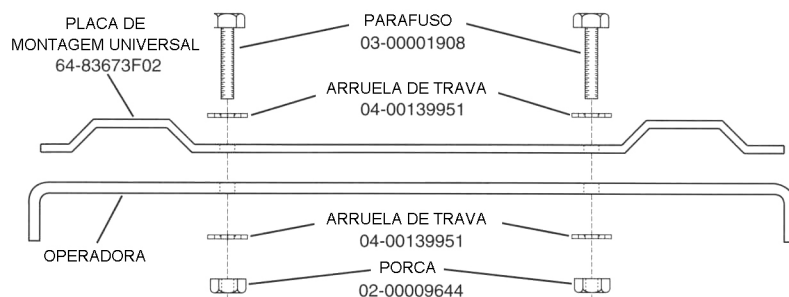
Instalação da Placa de Montagem Universal (Peça do Kit de Compartimento de Rádio)
